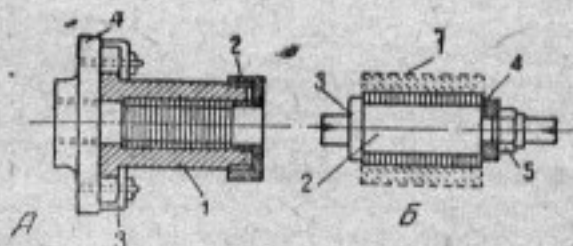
Приспособления для расточки внутренней поверхности колец (А) и сборки колец для наружной проточки после разрезки замка (Б)
